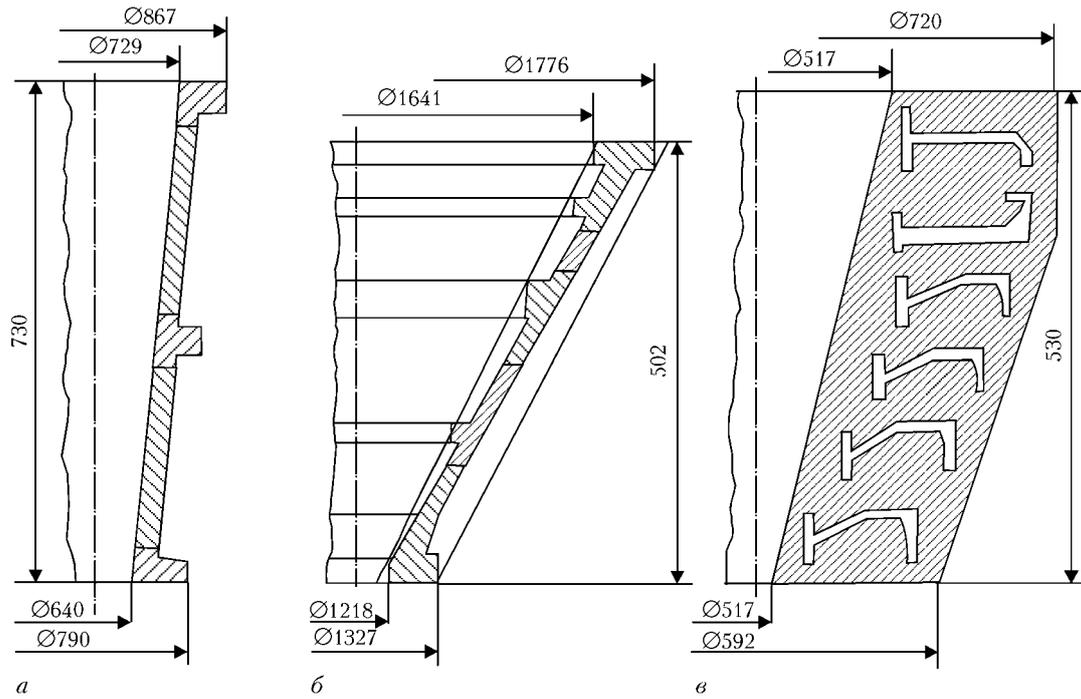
Эскизы корпусных сварных конструкций компрессора (а), турбины (б), литой заготовки (в), предназначенной для нескольких колец спрямляющего аппарата газовой турбины
